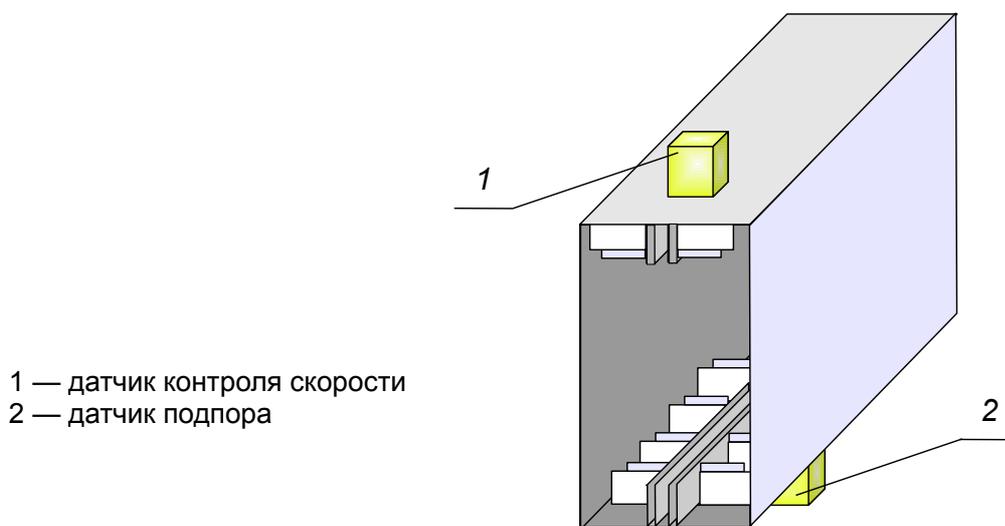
Установка датчиков обрыва цепи и подпора скребкового конвейера
